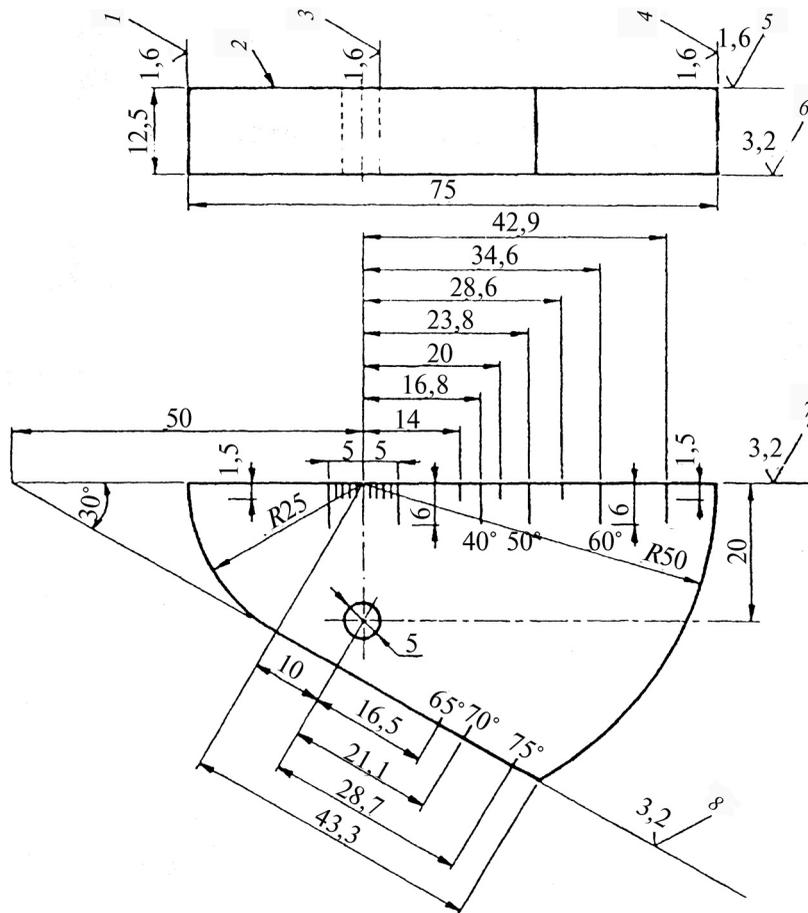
1 — шлифованная цилиндрическая поверхность; 2 — отражающая поверхность; 3 — обработанная поверхность отверстия; 4 — шлифованная цилиндрическая поверхность; 5 — шероховатость; 6, 7, 8 — фрезерованная поверхность
